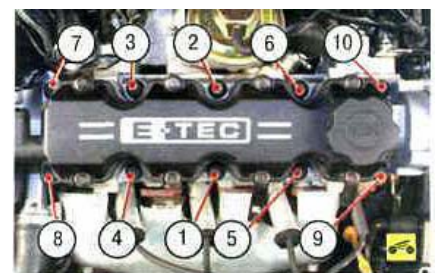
Последовательность затяжки болтов крепления головки блока цилиндров
